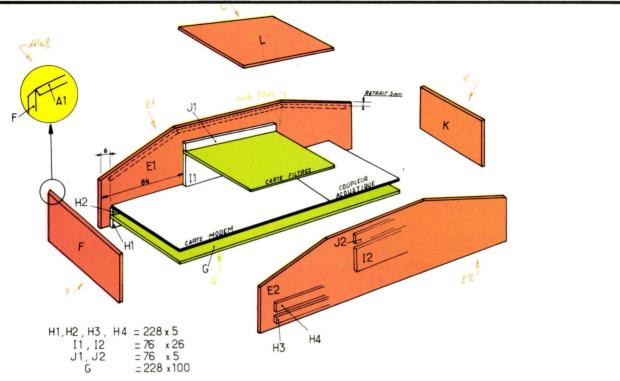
Fig. A. - Vue éclatée du boîtier. Remarquez la disposition des cartes électroniques disposées dans leurs glissières.
